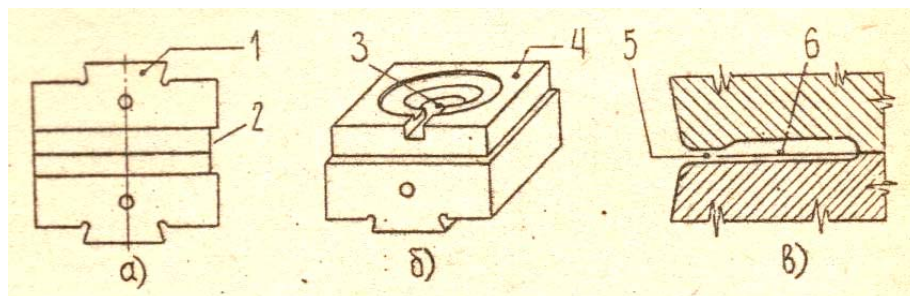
Конструкция молотового штампа: а — штамп в сборе; б — нижний штамп; в — облойная канавка; 1 — ласточкин хвост; 2 — контрольный угол; 3 — ручей; 4 — зеркало; 5 — мостик; 6 — магазин
